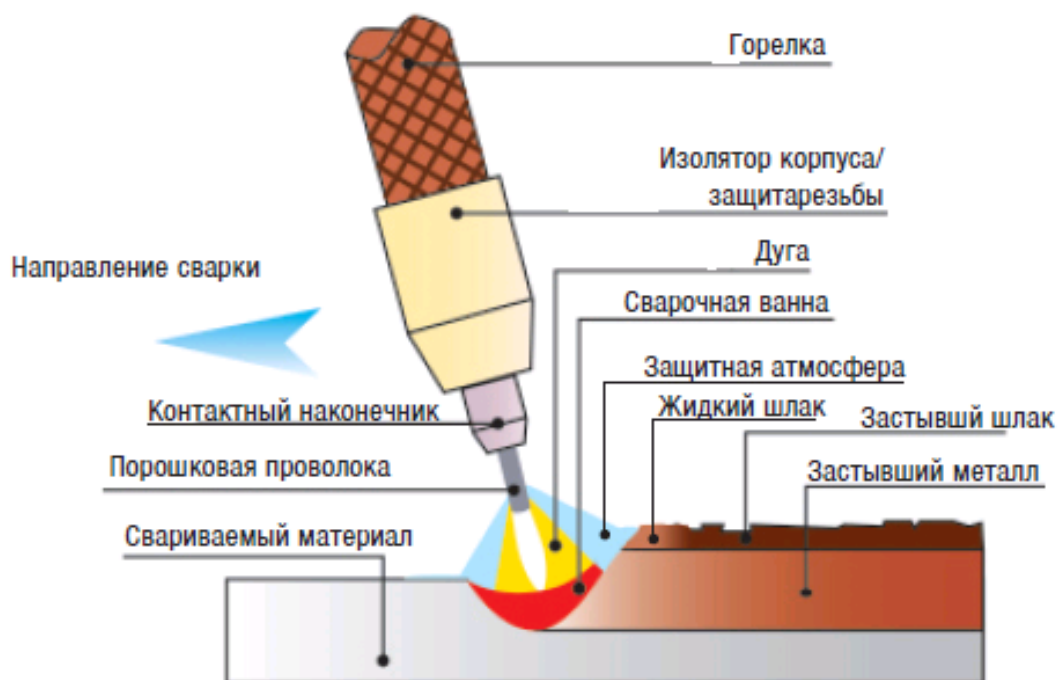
Схема дуговая сварка с использованием порошковой проволоки
